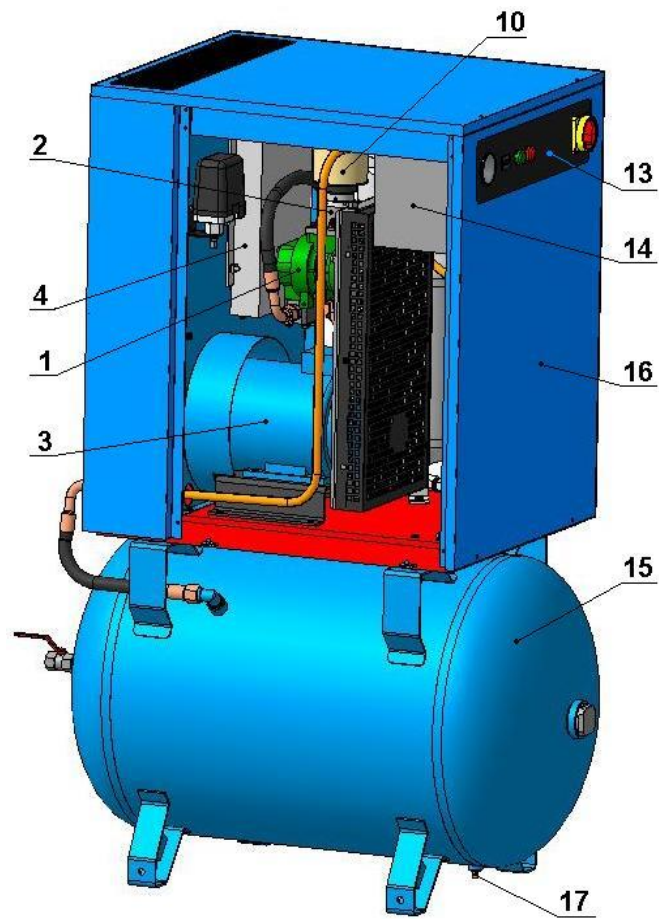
Общий вид компрессорной установки ВК5-...-270, ВК7-...-270, ВК10-...-270
